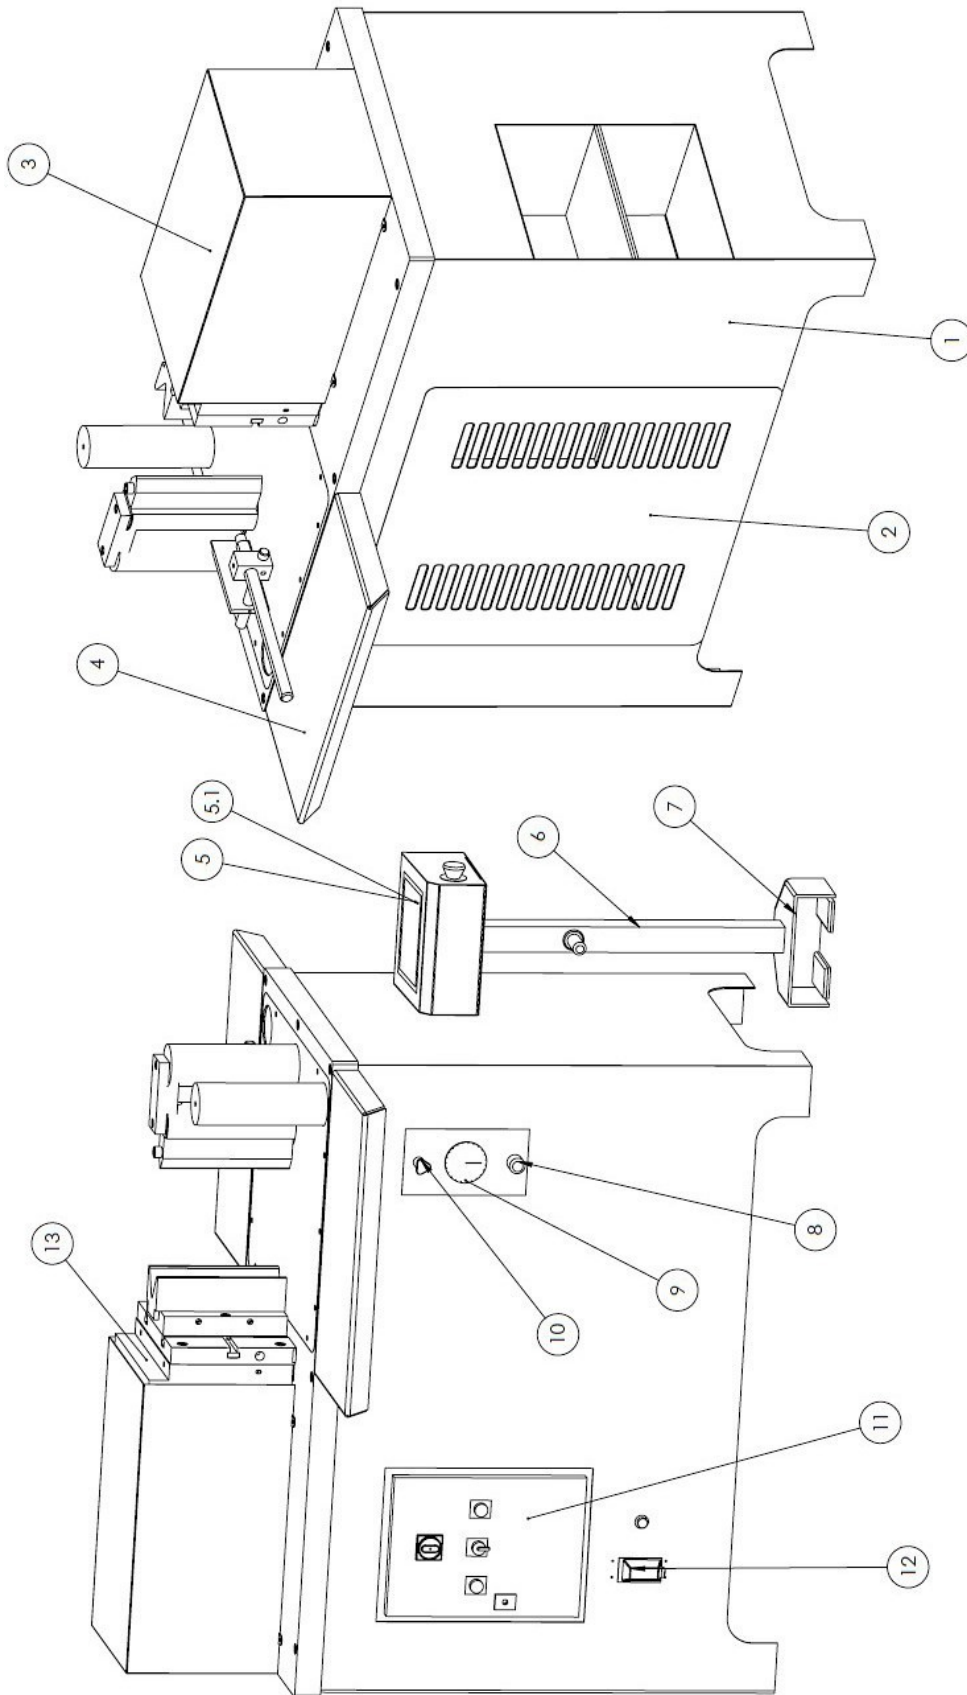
Dessin des pièces 1 Machine complète HBP 30
